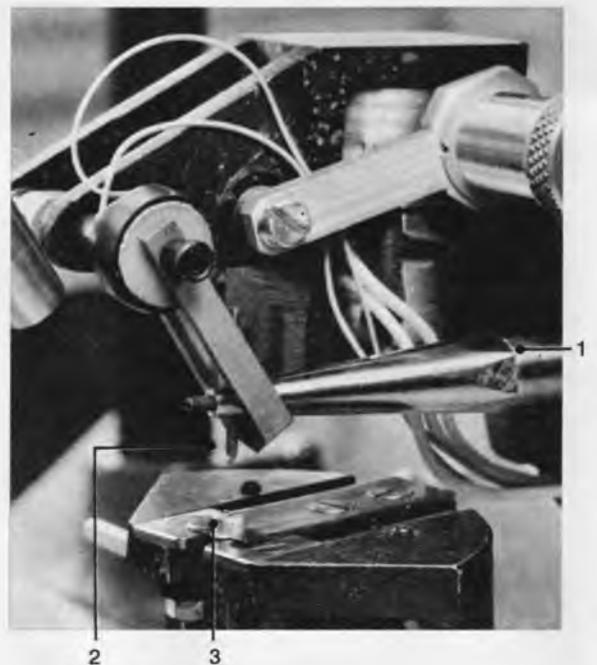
Der Schwingrüssel und das Schweißwerkzeug der Ultraschall-Schweißvorrichtung [6]. 1 = Metallstab (Rüssel); 2 = Schweißwerkzeug; 3 = Bodenplatten-Aufnahme
